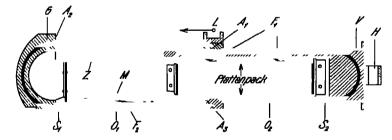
Konstruktionsschema einer Plattenwechselkassette
